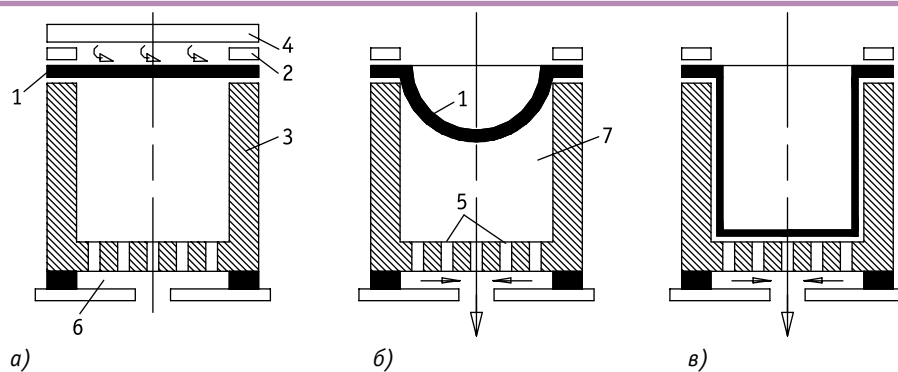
Схема вакуум-формування: стадії затискання та нагрівання полімерної заготовки (а); стадії герметизації та початку формування (б); стадії кінцевого формування та охолодження виробу (в) (1 — формований лист; 2 — притискна рама; 3 — матриця; 4 — нагрівач; 5 — вентиляційні канали; 6 — вакуумна порожнина матриці; 7 — порожнина, що оформляється)
